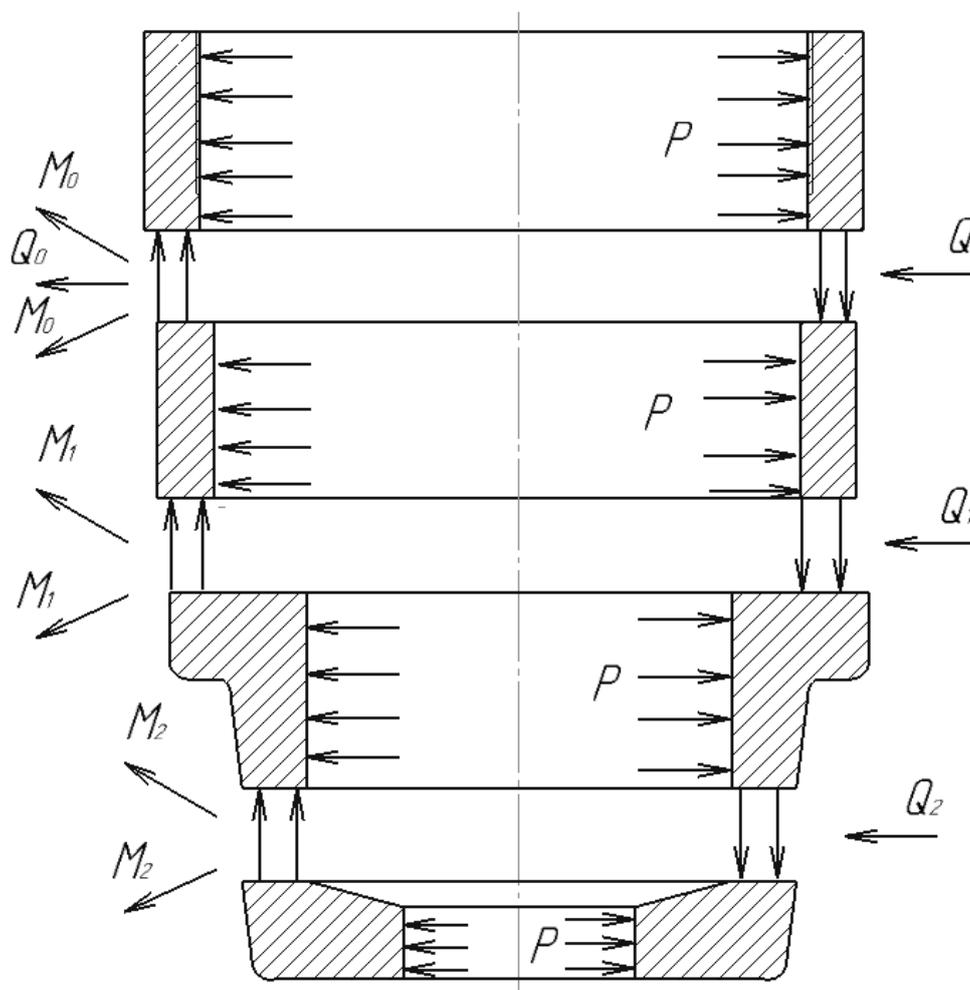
Схема для розрахунку корпусу превентора
